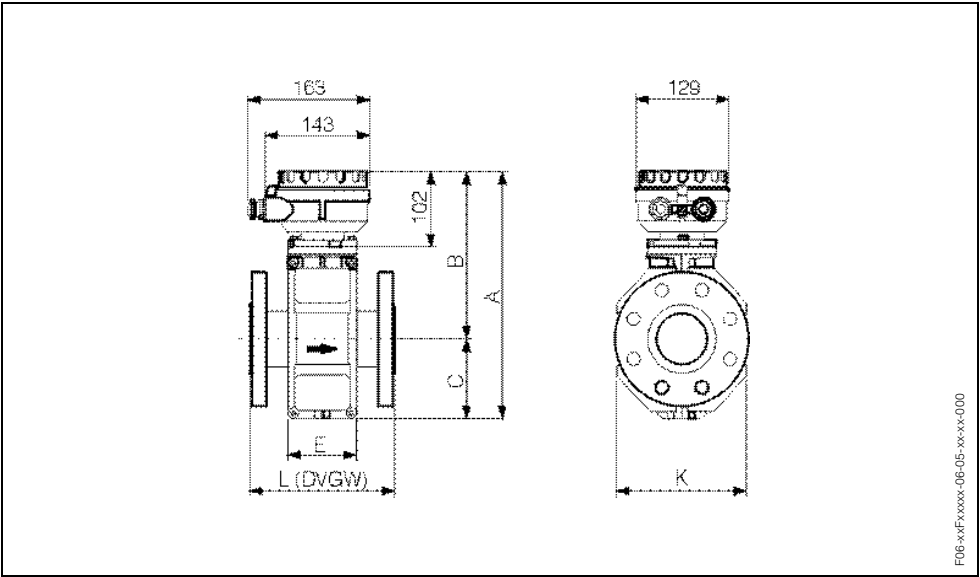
Dimensiones del Promag W / DN ≤ 300 (versión separada)
